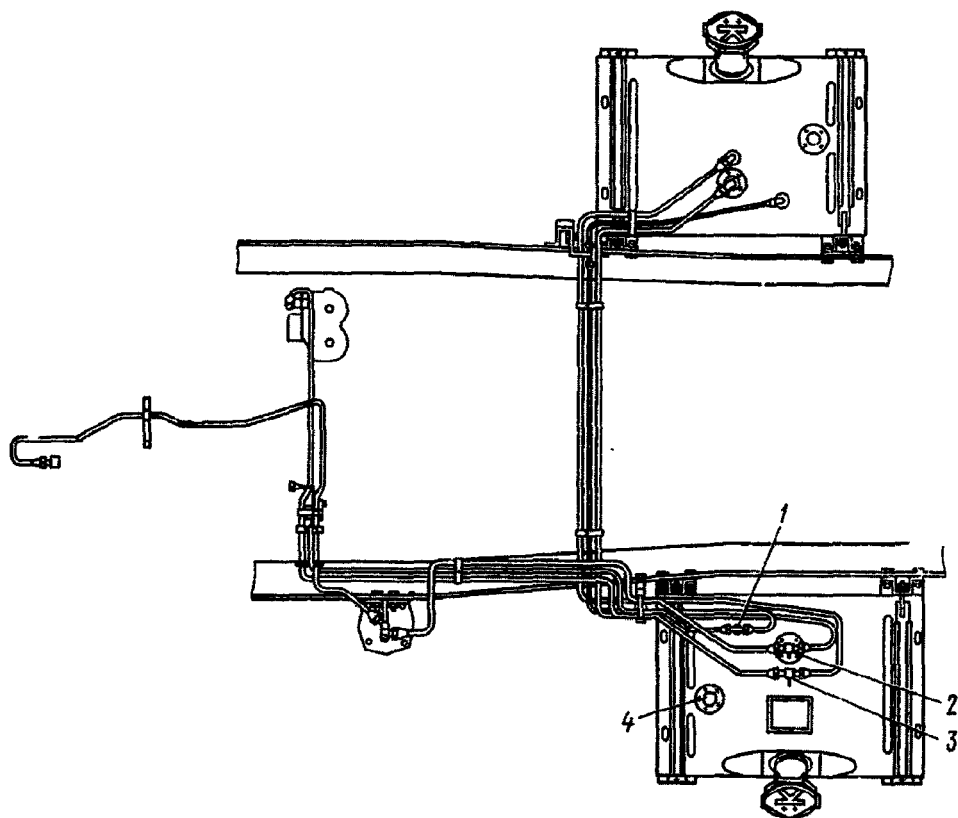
Установка топливных баков на автомобиле КамАЗ-4310:
